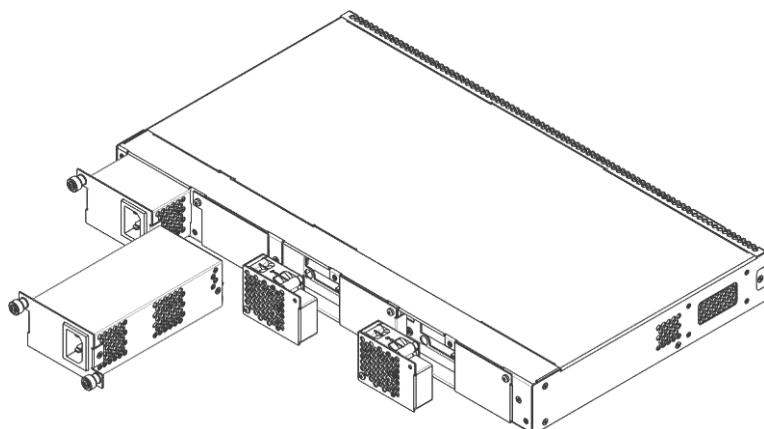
а – Блок вентиляции SMG-1016M. Крепление в корпус
